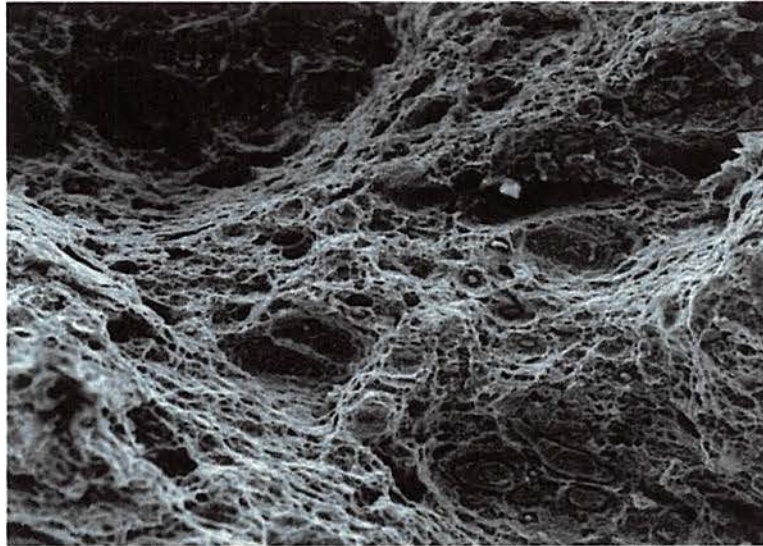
Aspecto da fratura dos corpos de prova situados no Metal de Solda da junta soldada do aço 2 ¼ Cr 1 Mo ensaiados a temperatura de 538 °C; MEV 200x
